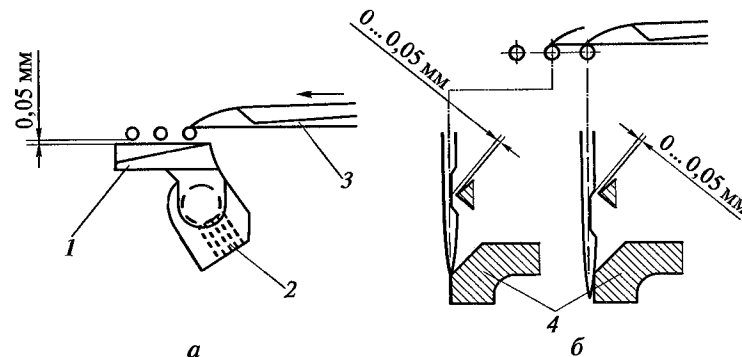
Установка положений отражателя (а) игольной петли и стабилизатора (б) положения игл
